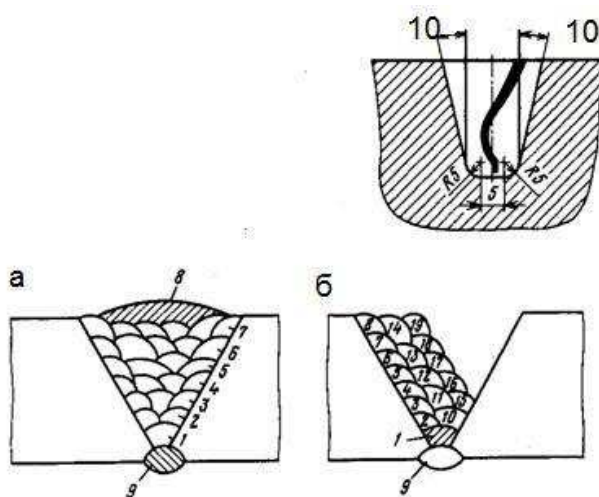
Схема разделки несквозных трещин, а также последовательность (показана цифрами) сварка стыка *a* и заварка трещин *б* при многослойной сварке.
